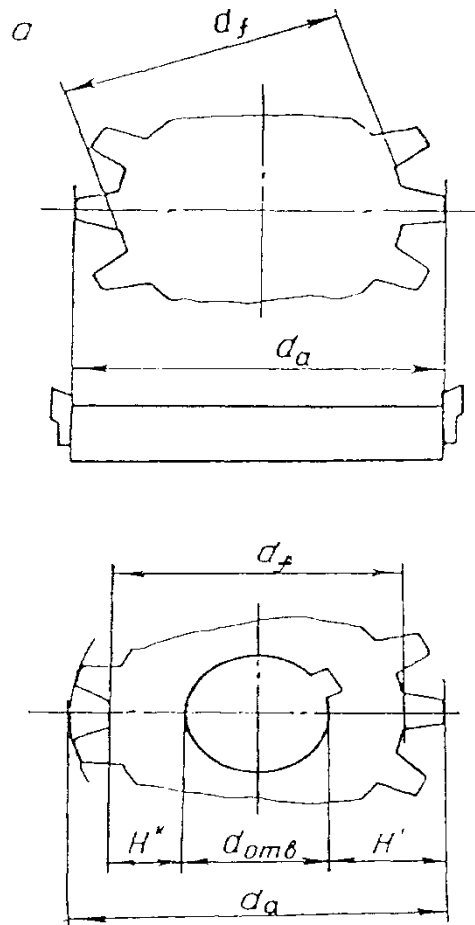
Схема обмера диаметров вершин (d_a) и впадин (d_f) зубчатого колеса:
